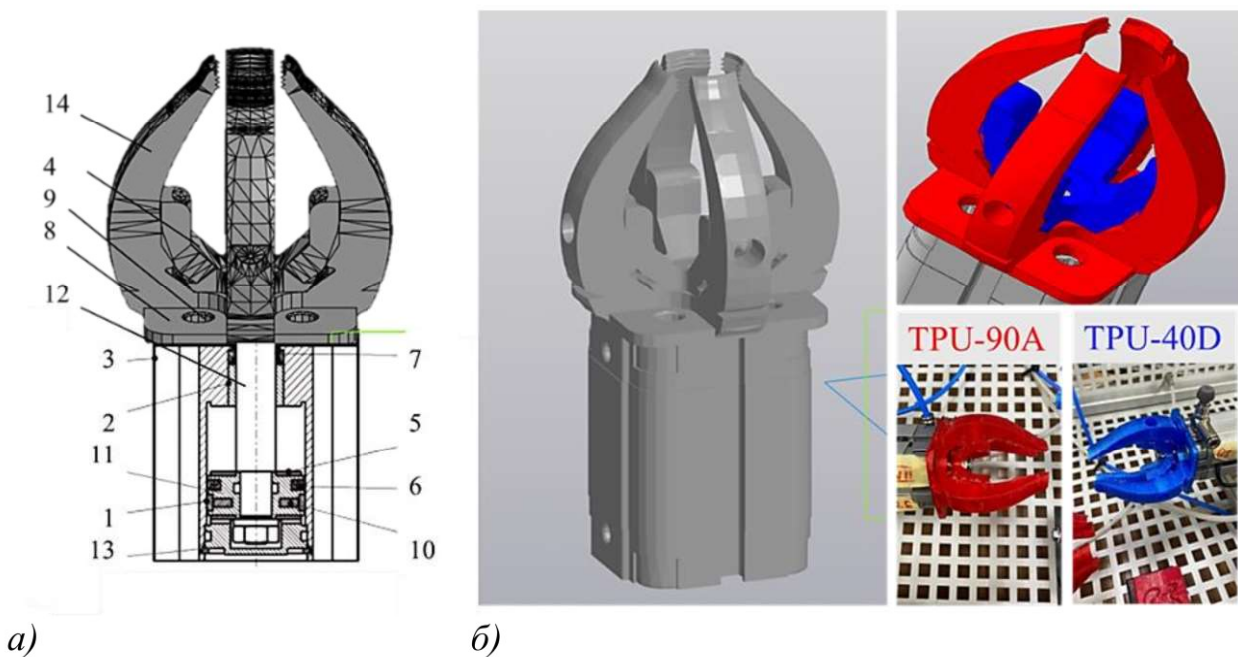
Загальний вигляд випробуваних м'яких захватів, виготовлених із ТПУ-90А та ТПУ-40Д методом 3D-друку: збірка м'якомехатронних механічних захватів (а); система м'якого захвата для розкриття щелеп на 60° та загальний вигляд авторського м'якого захвата, надрукованого на 3D-принтері (гнучка термопластична поліуретанова нитка та PLA із шовковою ниткою) (б)
